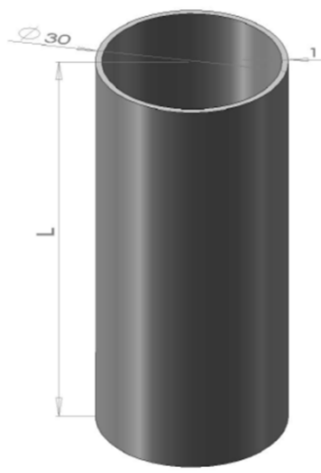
Les dimensions de structure tubulaire à section cylindrique.
